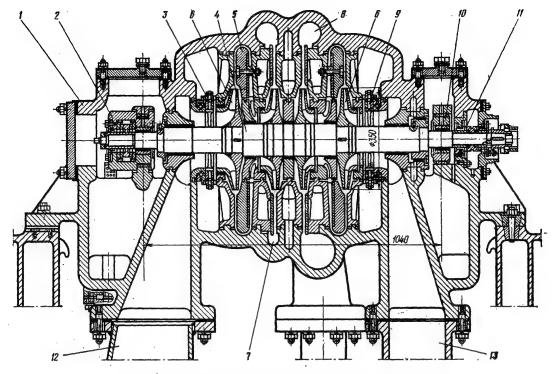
Пропановый центробежный компрессор ТКП-435:
